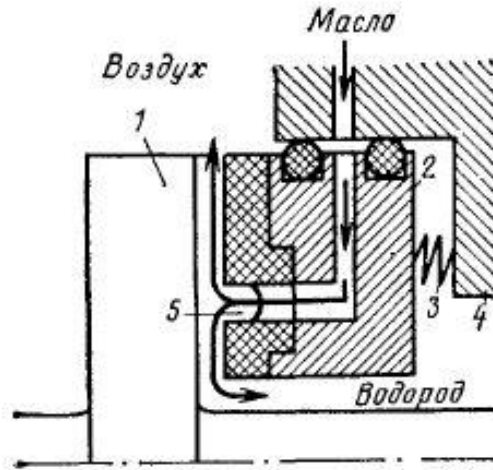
Торцевое уплотнение: 1 — диск на валу ротора; 2 — вкладыш; 3 — пружина; 4 — корпус; 5 — кольцевая канавка
